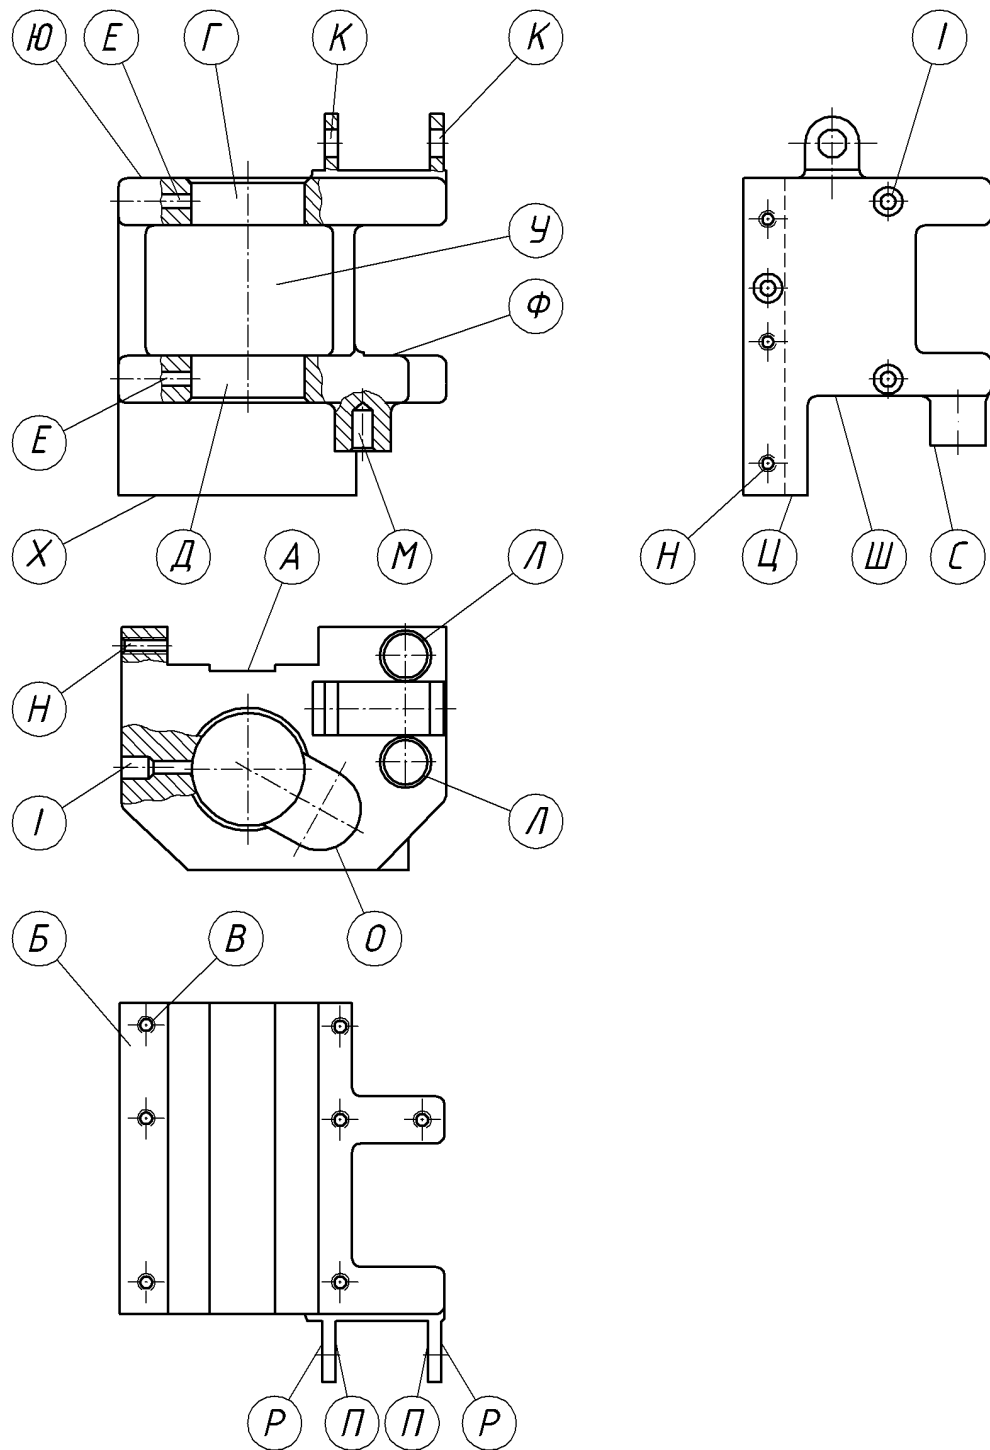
Ескіз деталі з позначеними поверхнями
